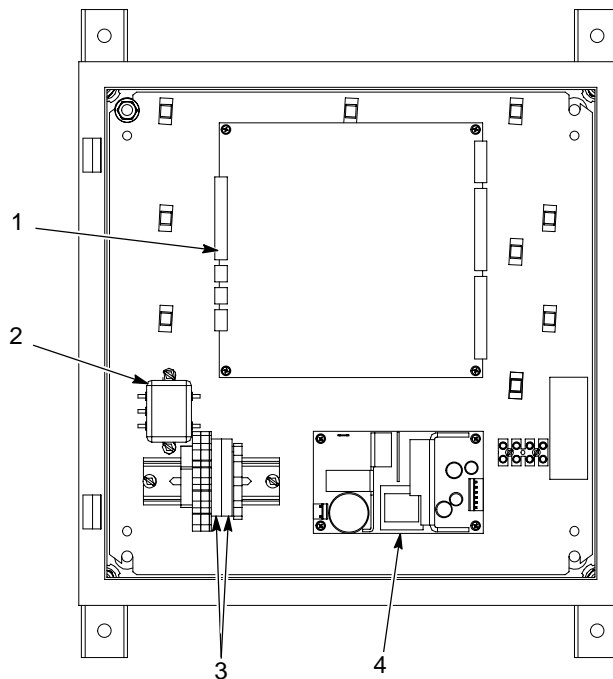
Pièces de rechange pour Passerelle API Prodigy
